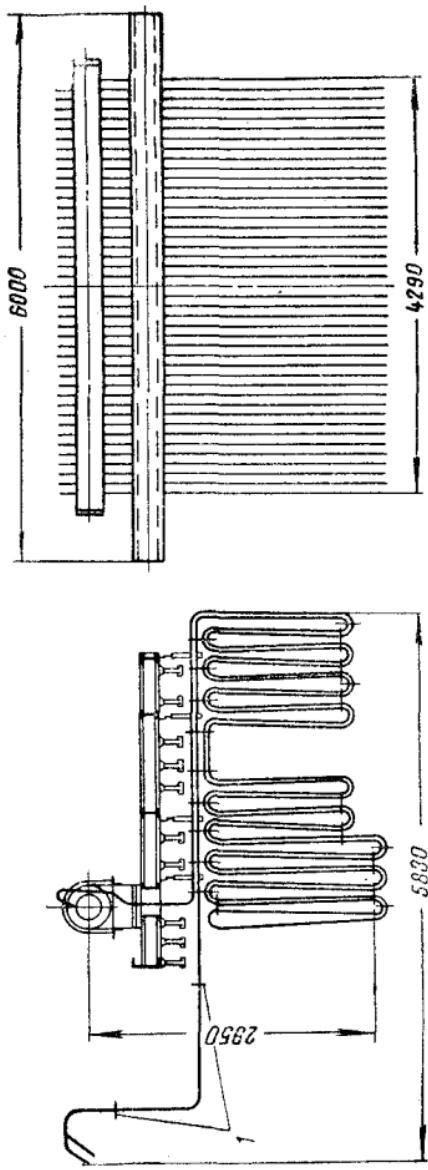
Задний пакет паропреревателя со щитом ЩП-4
